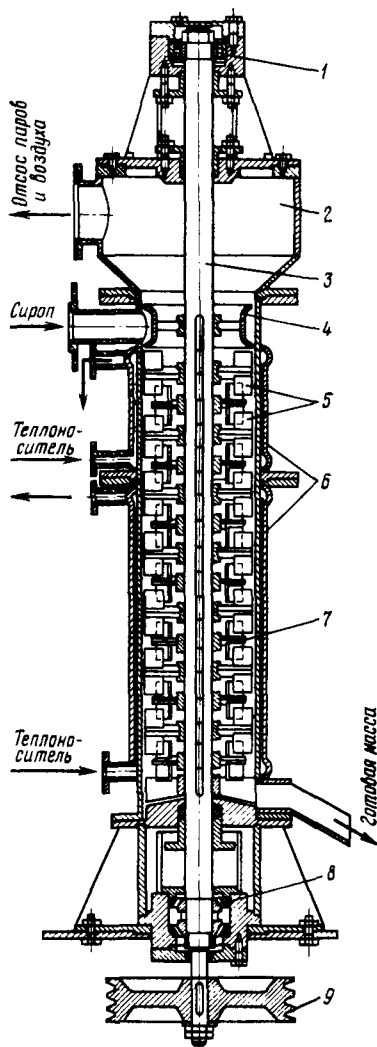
Роторный пленочный аппарат-кристаллизатор
